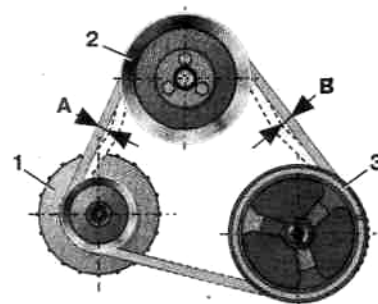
Схема проверки натяжения ремня привода насоса
